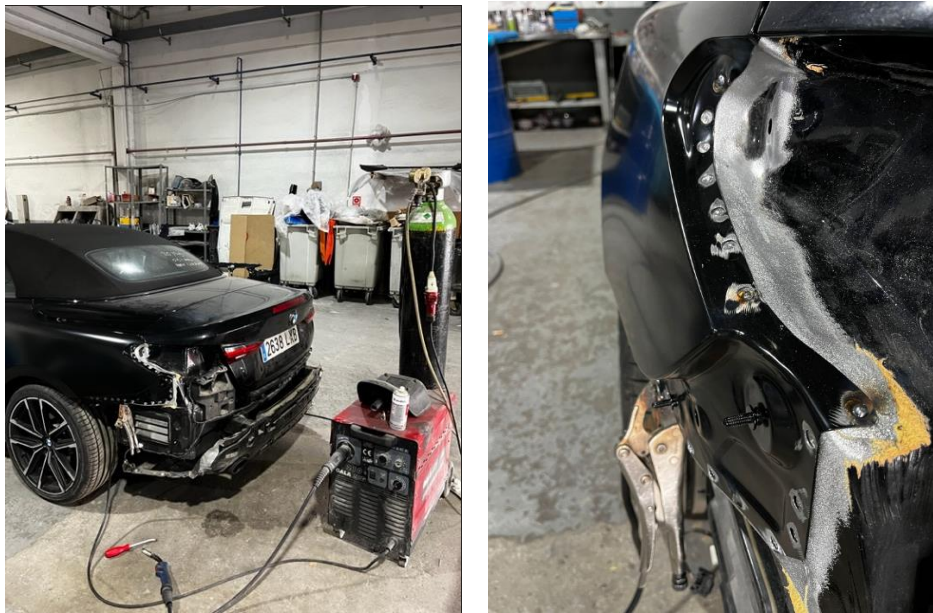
Aplicación puntos de soldadura, conformado chasis.
